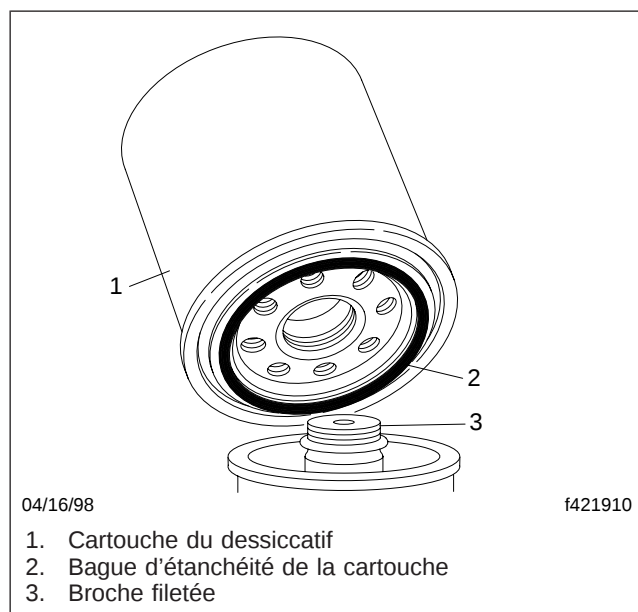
, Remplacement de la cartouche du dessiccateur AD-IS
